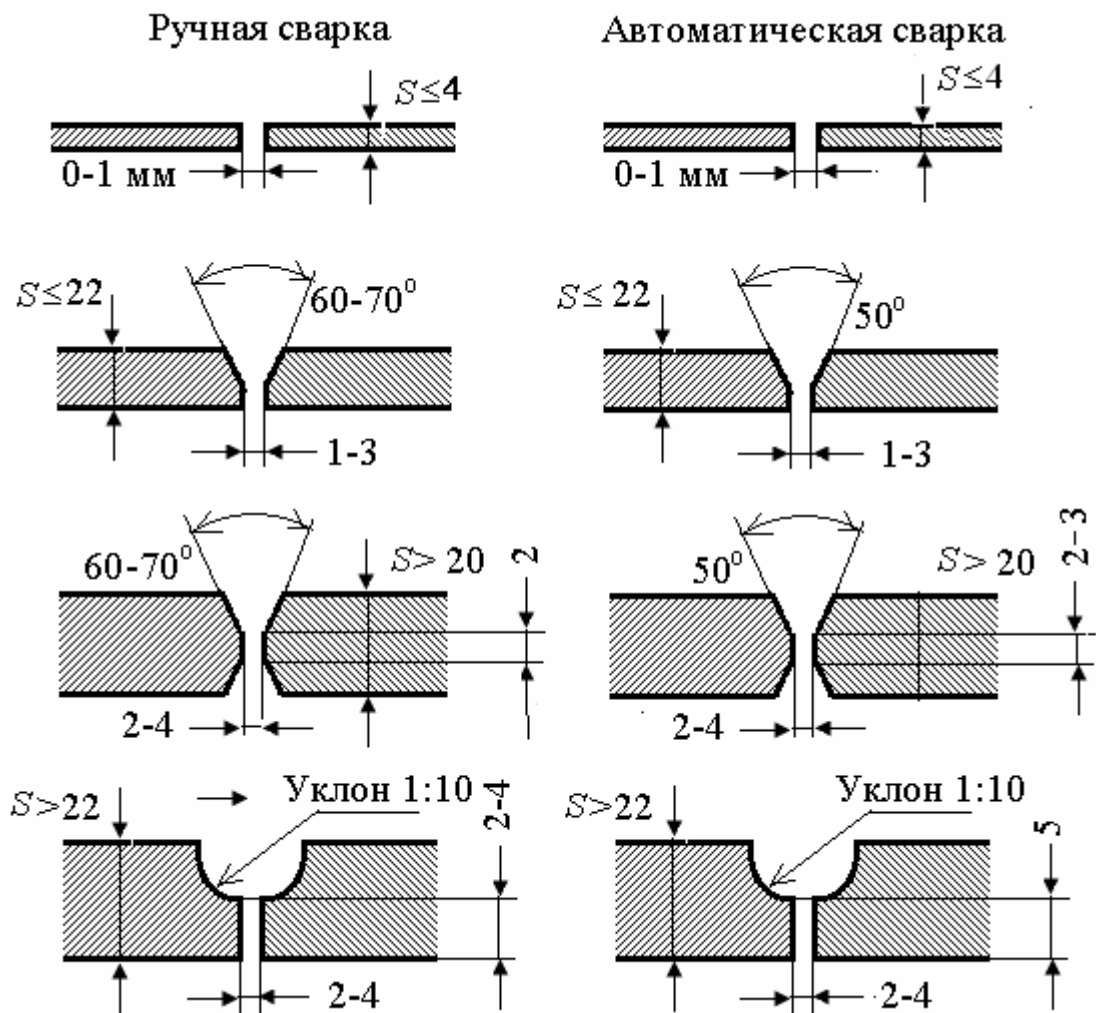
Способы подготовки кромок под сварку
